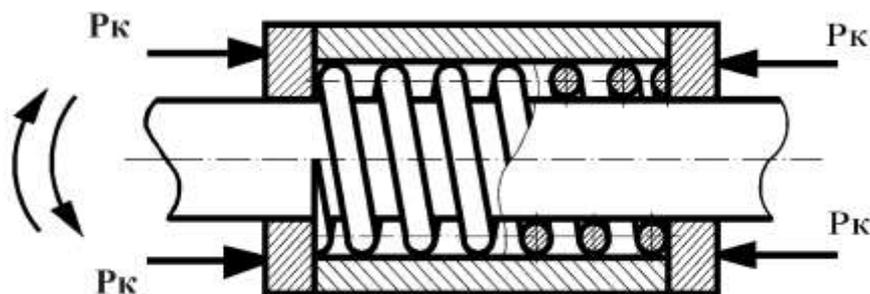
Схема подшипника с подвижным пружинным вкладышем
